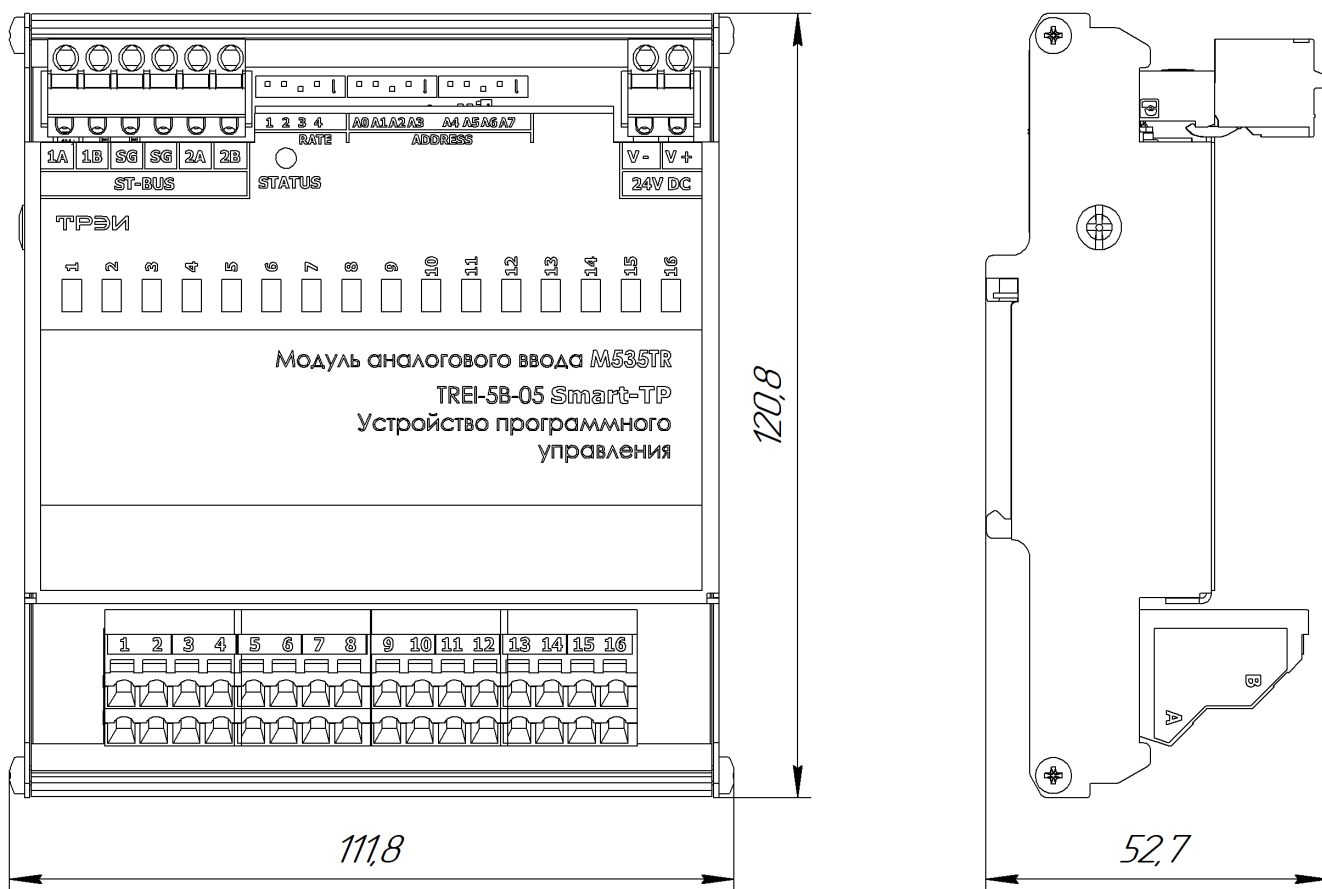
Чертеж общего вида M535TR с указанием габаритных и присоединительных размеров
